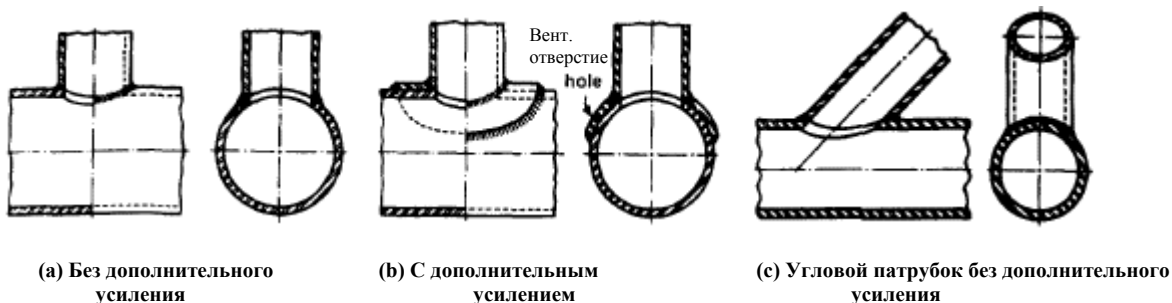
А, В, С. Типовые сварные патрубки.
